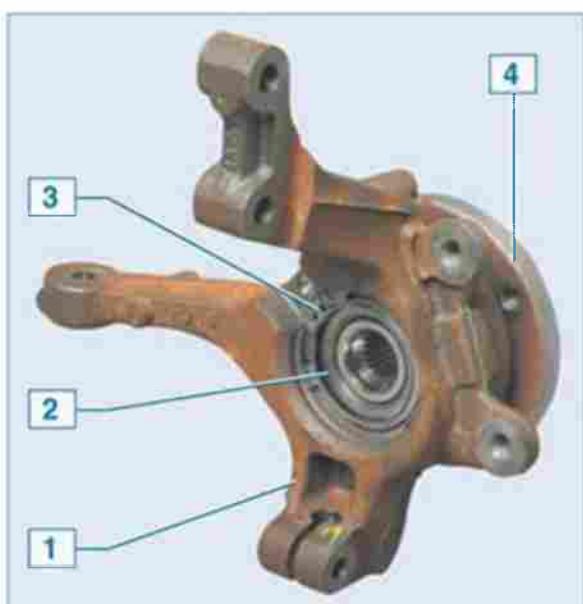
Ступичный узел переднего колеса: 1 - поворотный кулак; 2 - подшипник ступицы; 3 - установочное кольцо датчика скорости вращения колеса; 4 - ступица колеса.
